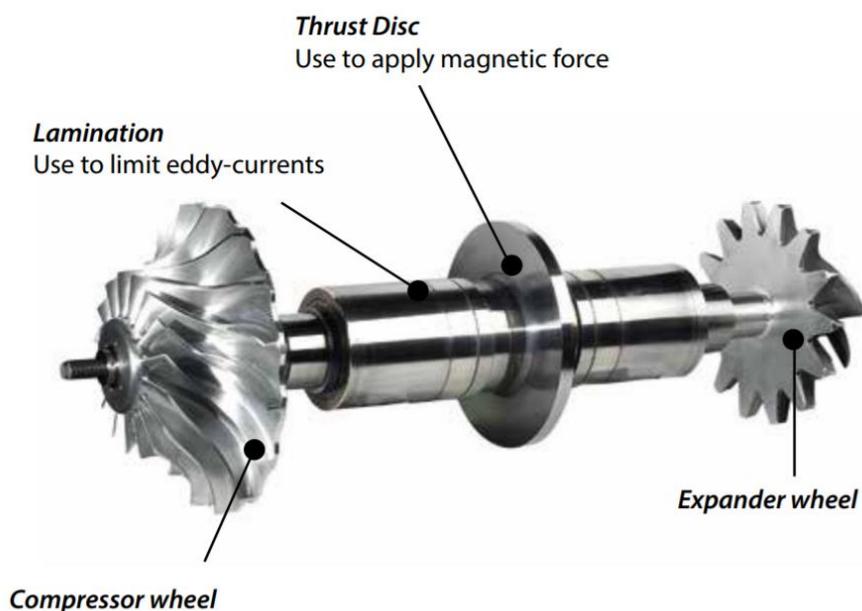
Ротор турбодетандерного агрегата, включающий в себя рабочие колеса компрессора и детандера [5]
